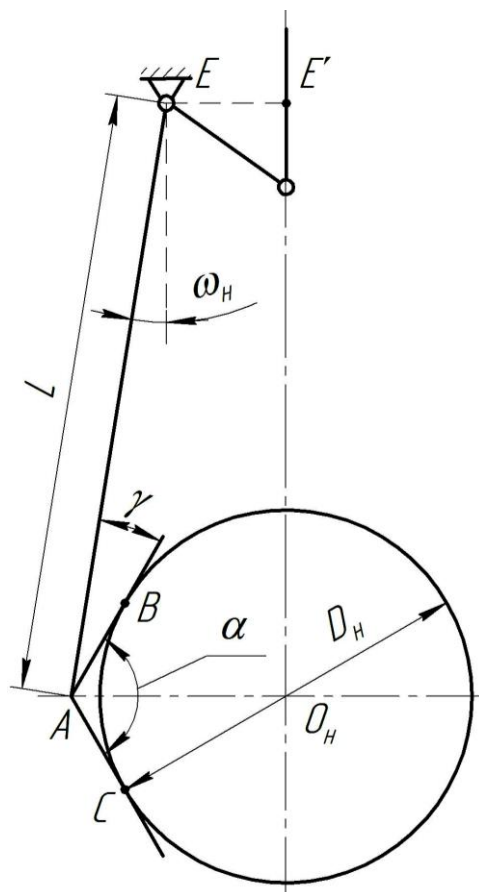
Розрахункова схема оцінки точності положення деталі в захватному пристрої
